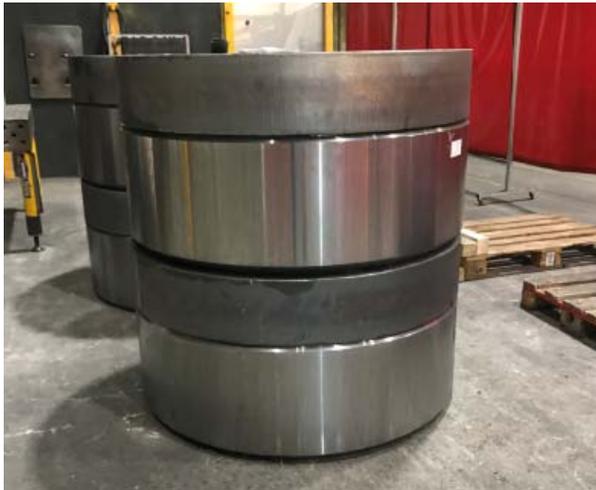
Mit einem Durchmesser von 2.270 Millimetern, einer Höhe von 1.391 Millimetern und 12 Tonnen Gewicht war jedes der vier Bauteile ein richtiger Koloss.
